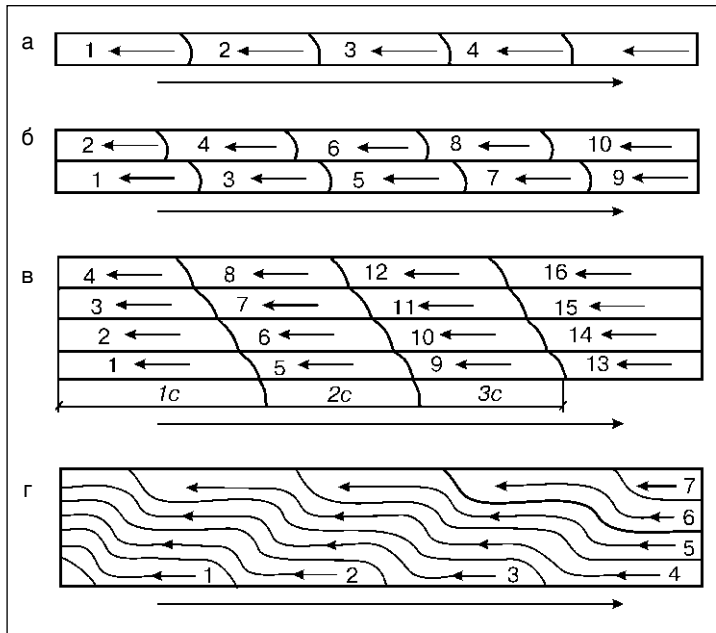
Способы выполнения швов ручной дуговой сваркой: а — обратно-ступенчатый; б — двойным слоем; в — секциями; г — «каскадом» (цифрами на а, б обозначен порядок наложения валиков, на в, г — обозначены слои)
